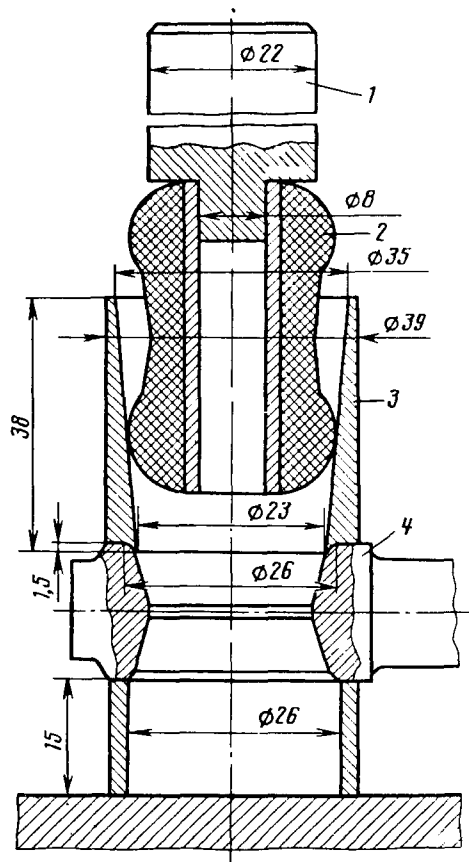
Приспособление для запрессовки резиновых шарниров в гнезда рулевых тяг:
